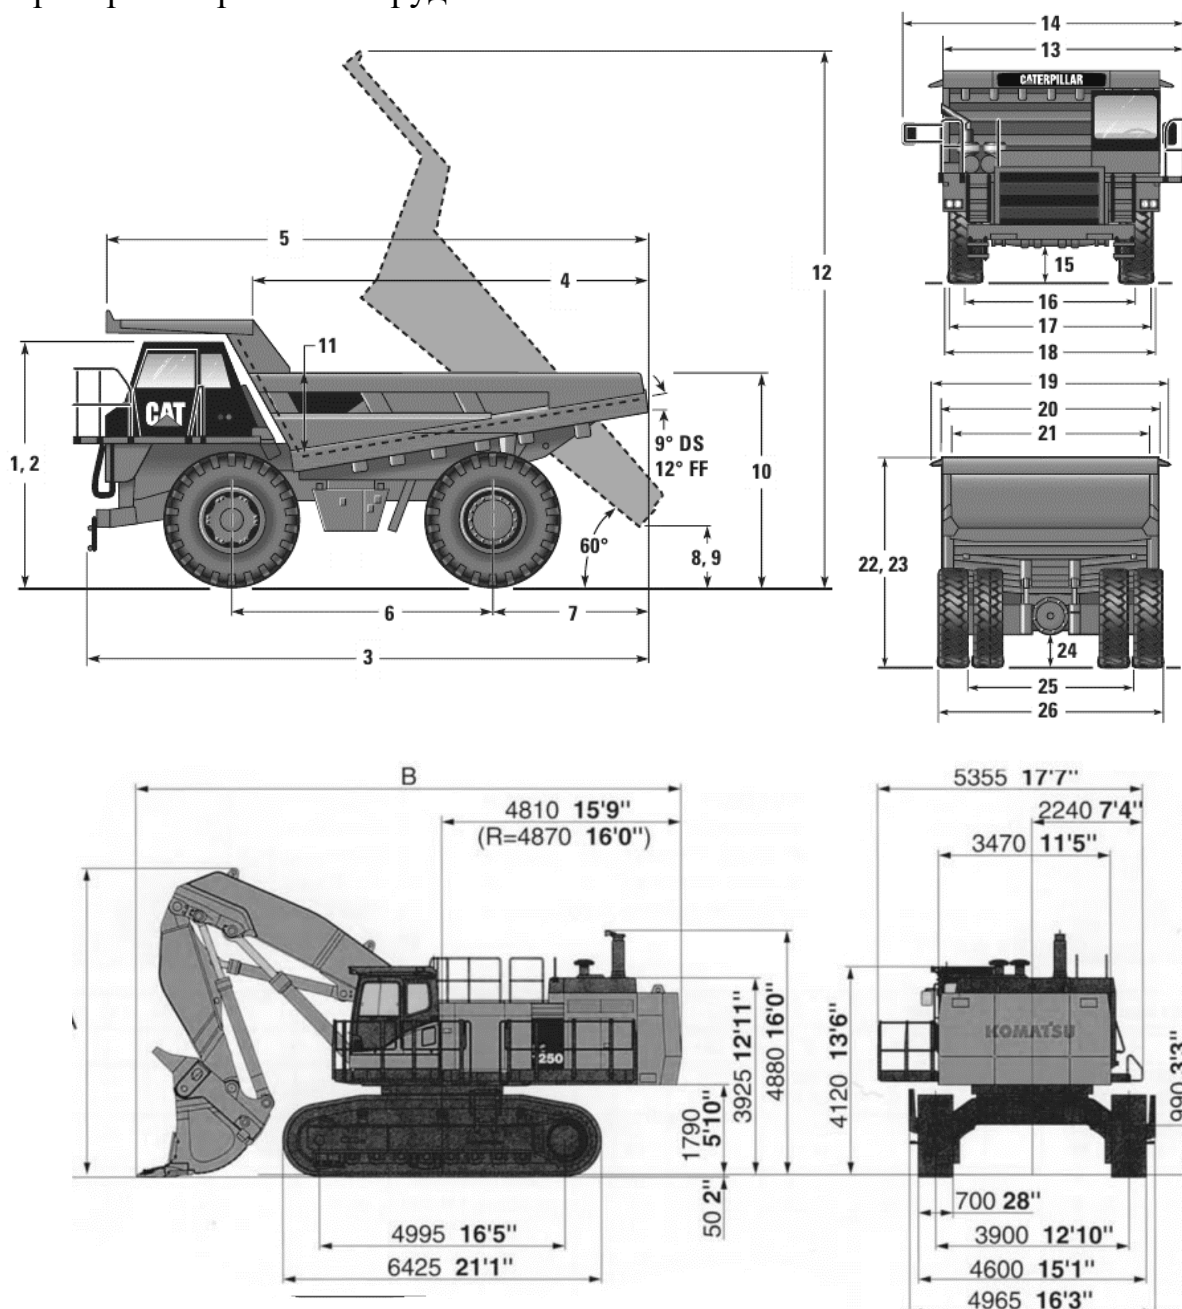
Габариты самосвала CAT 773 E и экскаватора Komatsu PC-1250
